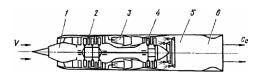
Схема ТРДФ: *I* — входное устройство (воздухозаборник); *2* — компрессор; *3* — основная камера сгорания; *4* — газовая турбина; *5* — форсажная камера сгорания; *6* — выходное устройство (реактивное сопло)
